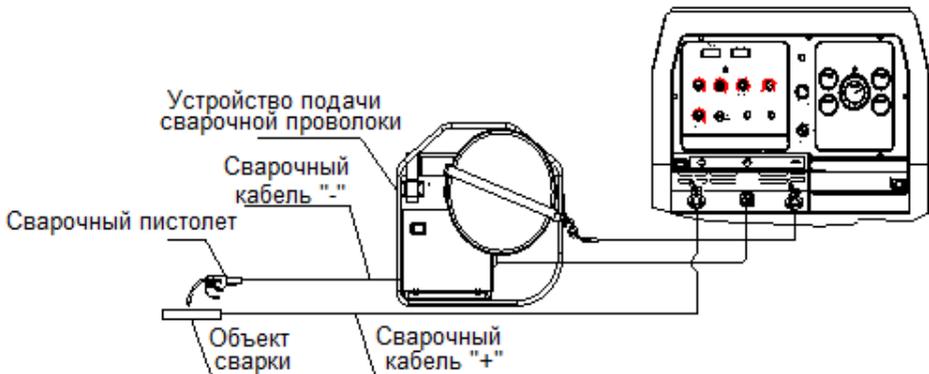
Схема подключения при сварке самозащитной проволокой.
